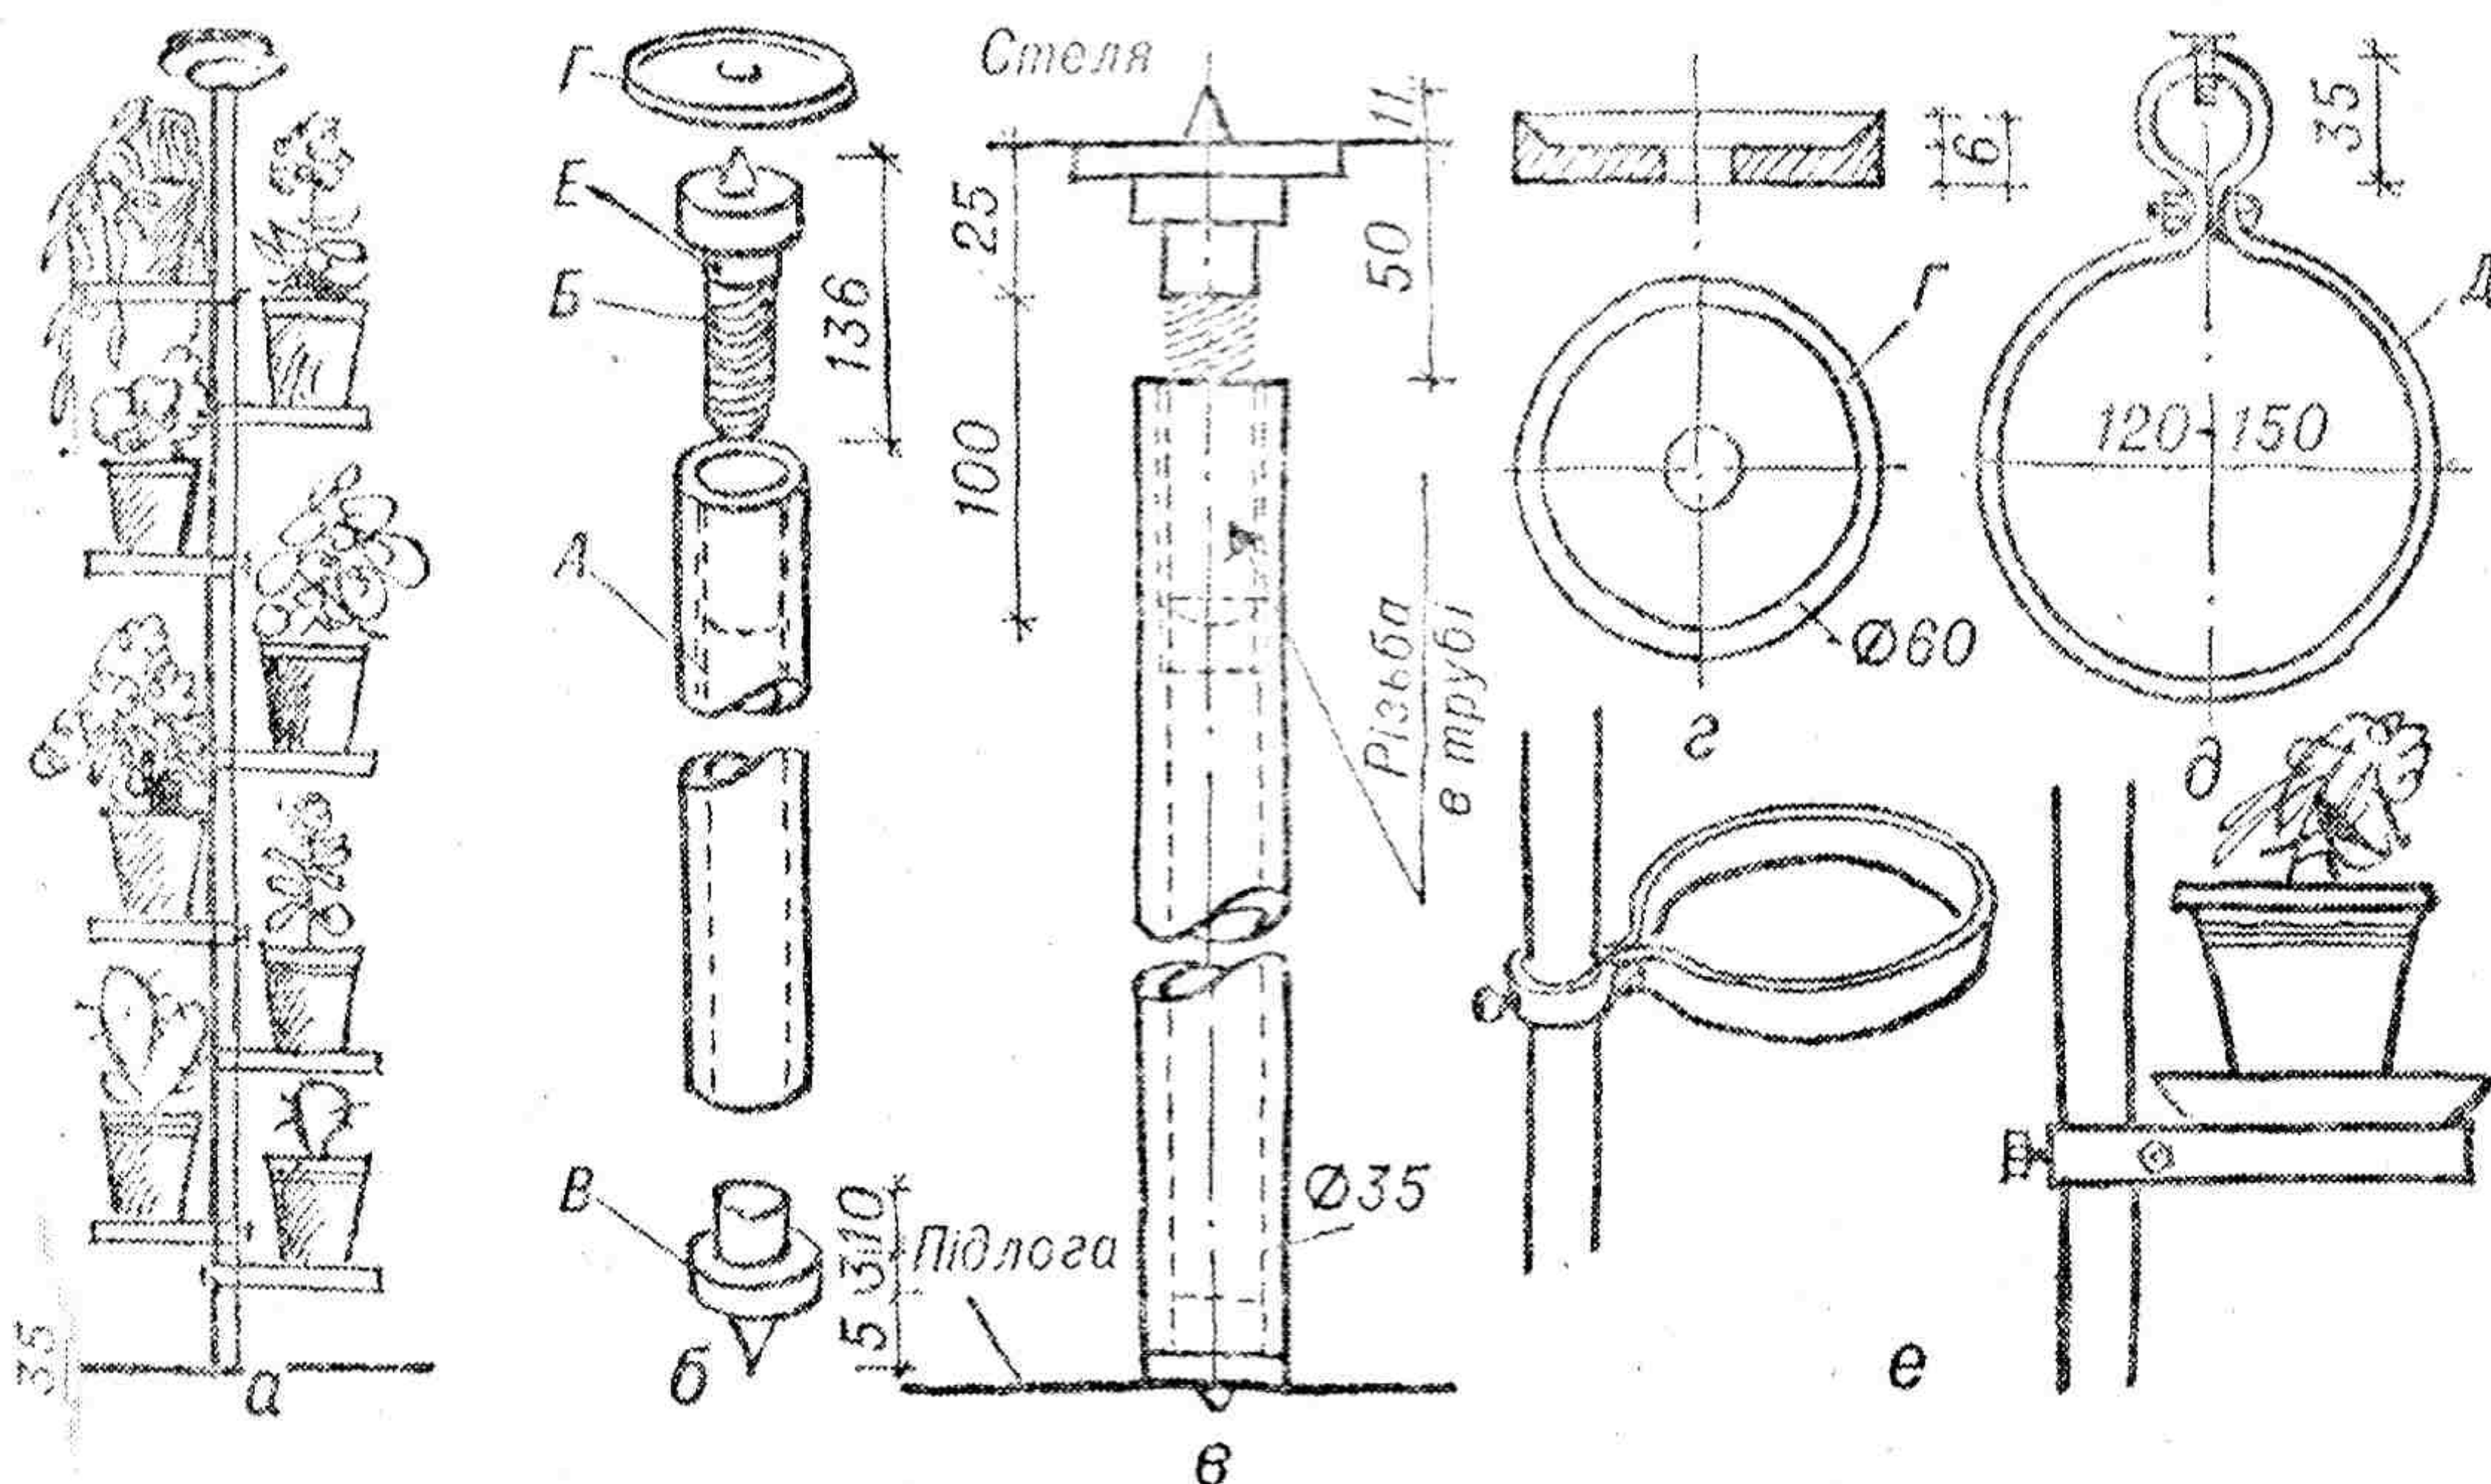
Металева підставка для квітів: а — загальний вигляд; б, в, г, д — деталі; е — кріплення деталі Д; А — труба; Б — деталь для фіксації підставки у вертикальному положенні; В — деталь для закріплення нижньої частини опори; Г — опорне кільце; Д — деталь для підтримування горщиків з квітами; Е — отвір.
